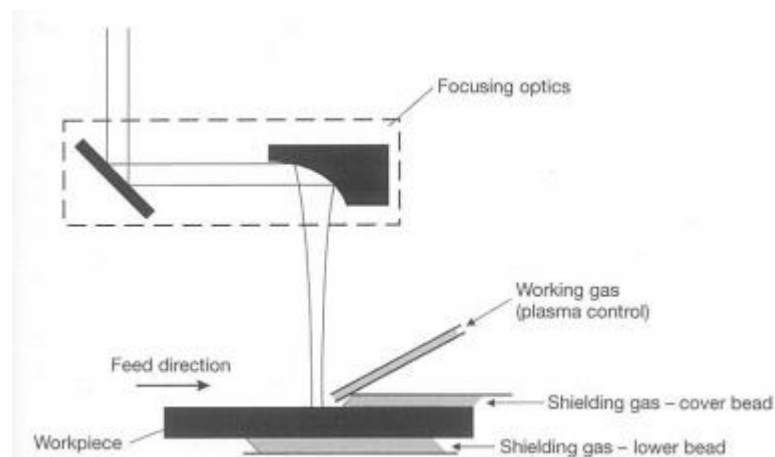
Processo de soldadura laser com um fornecimento de gás de proteção e de processo, [2].
